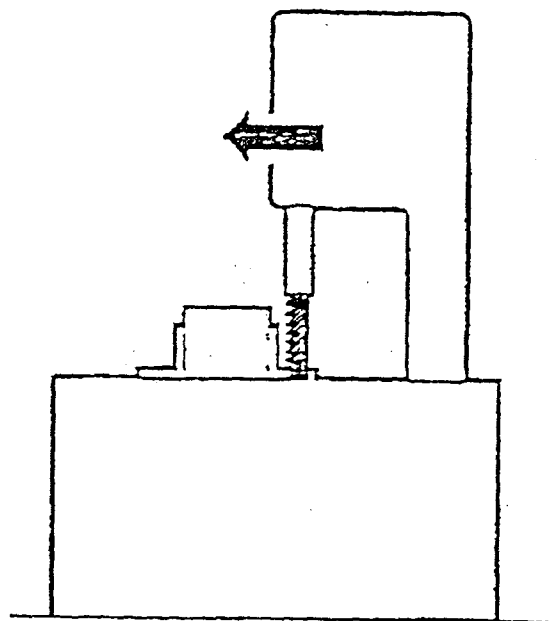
Вертикальний стрічковопиляльний верстат для фронтального різання
